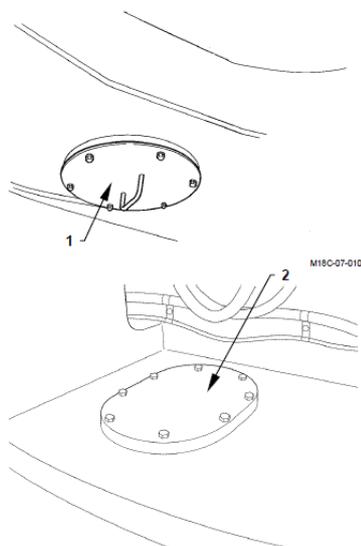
Смазка опорно-поворотного устройства
